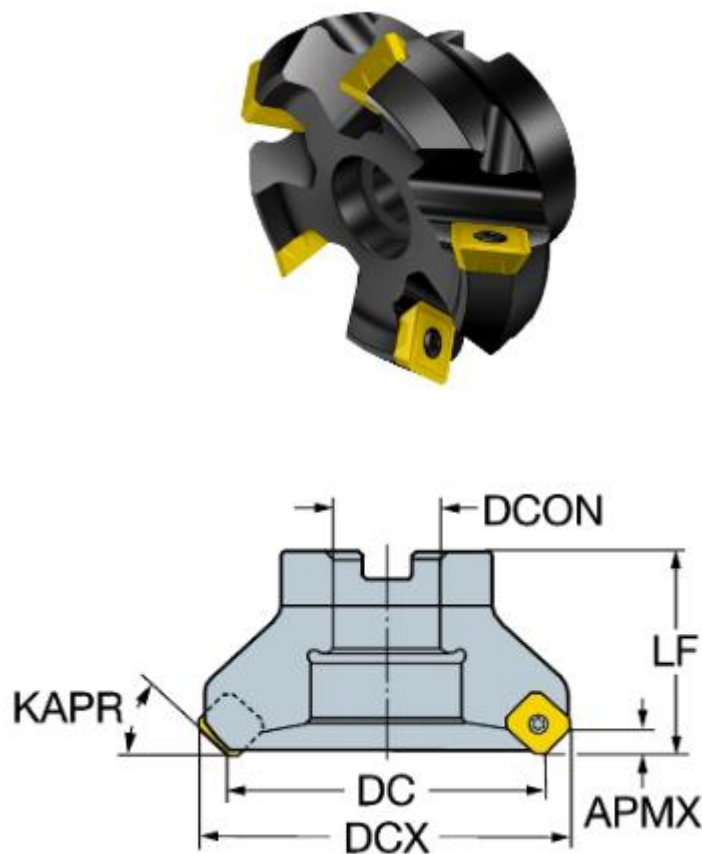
Торцева фреза CoroMill®245 фірми Sandvik Coromant
